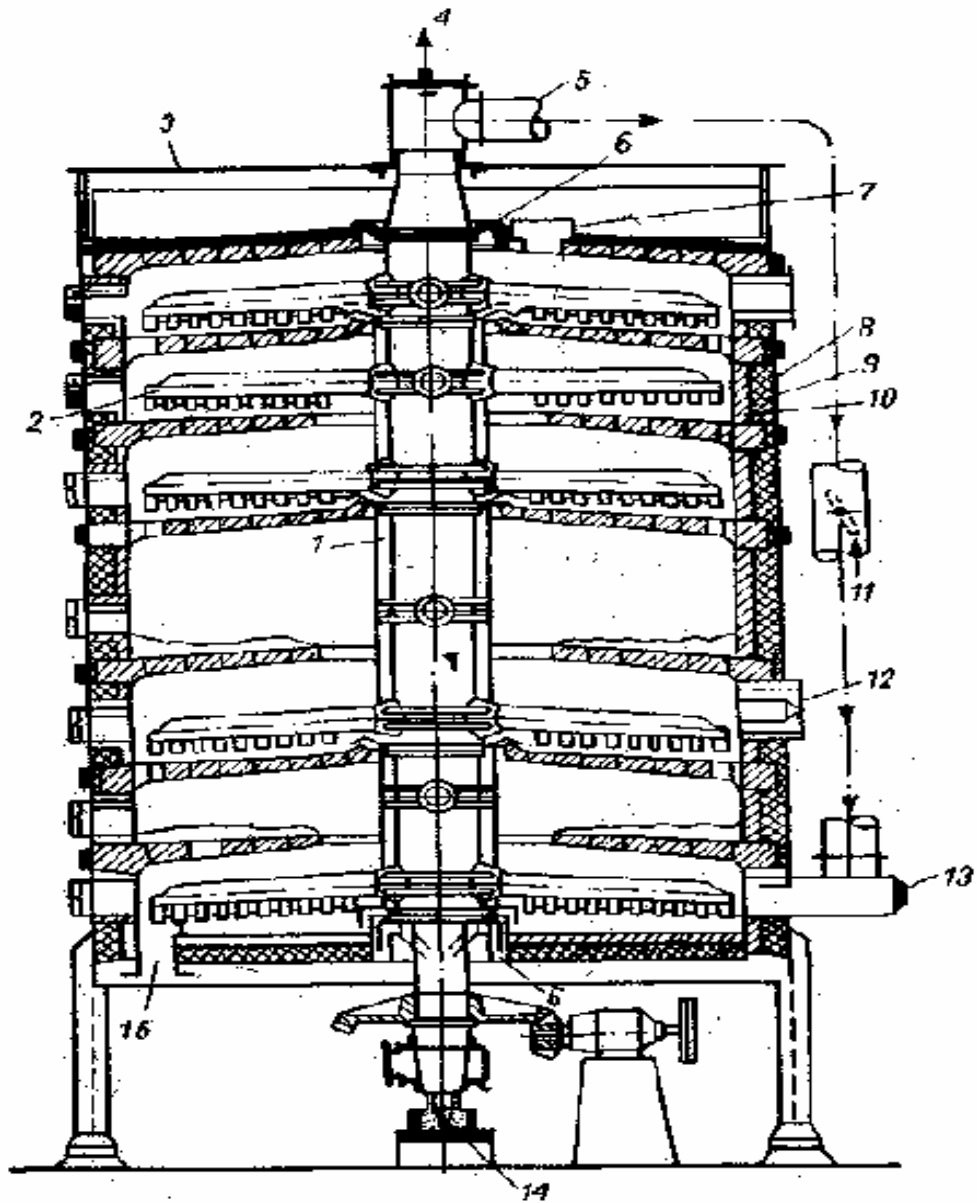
Поперечний переріз багатоподової печі "Херешоф":
